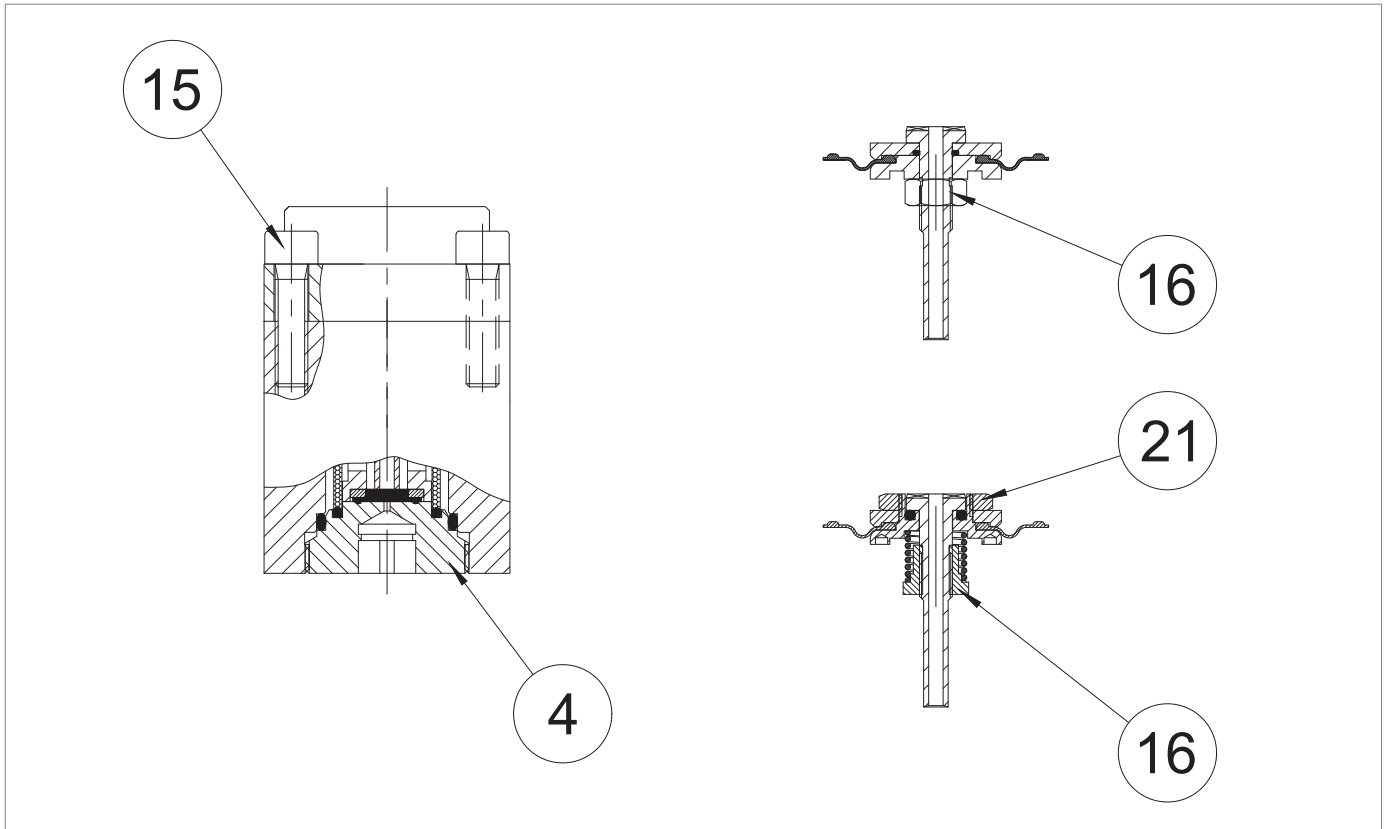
Coppie di serraggio pre-riduttore R14/A
